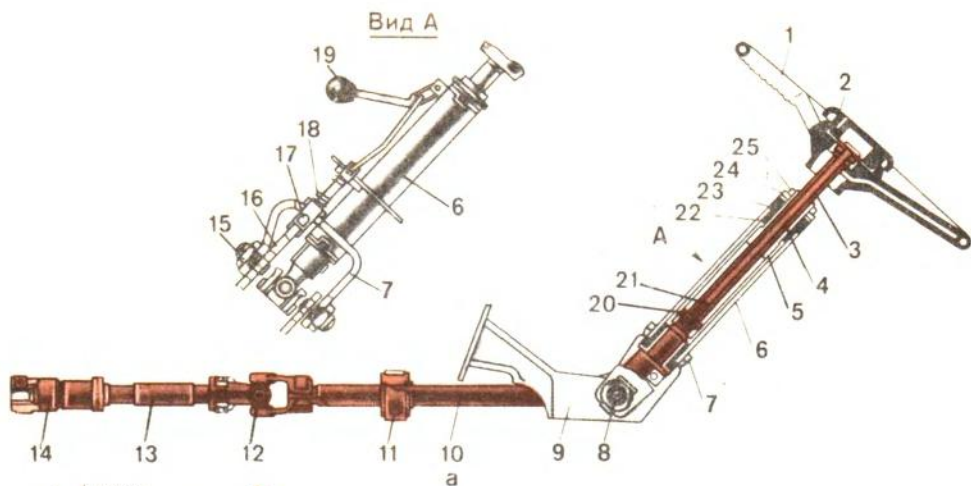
Привод рулевого механизма трактора МТЗ-80:
